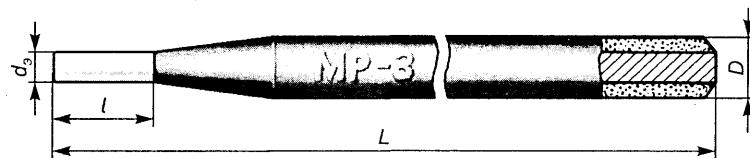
Покрытый электрод для ручной дуговой сварки
